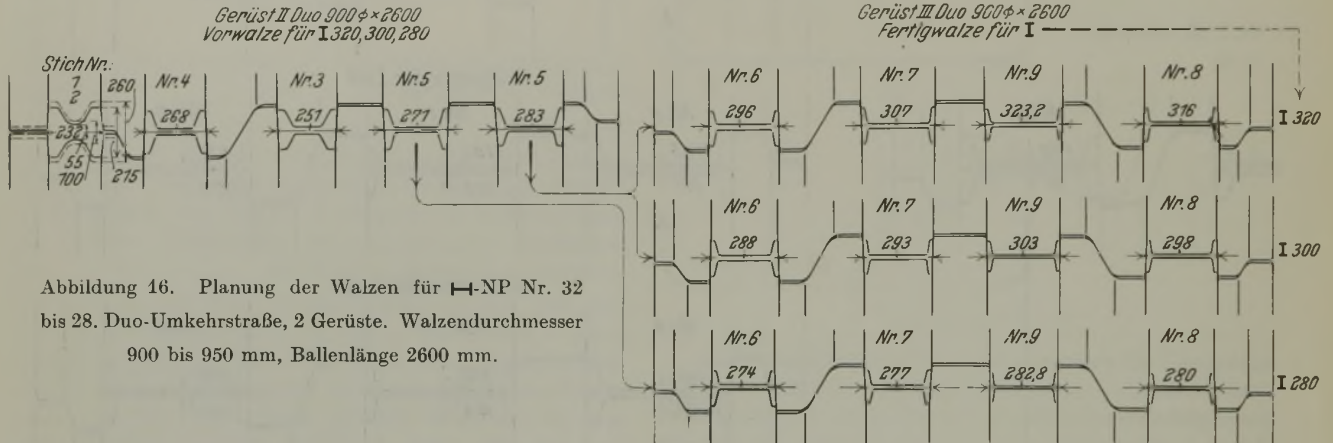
Planung der Walzen für H-NP Nr. 32 bis 28. Duo-Umkehrstraße, 2 Gerüste. Walzendurchmesser 900 bis 950 mm, Ballenlänge 2600 mm.
